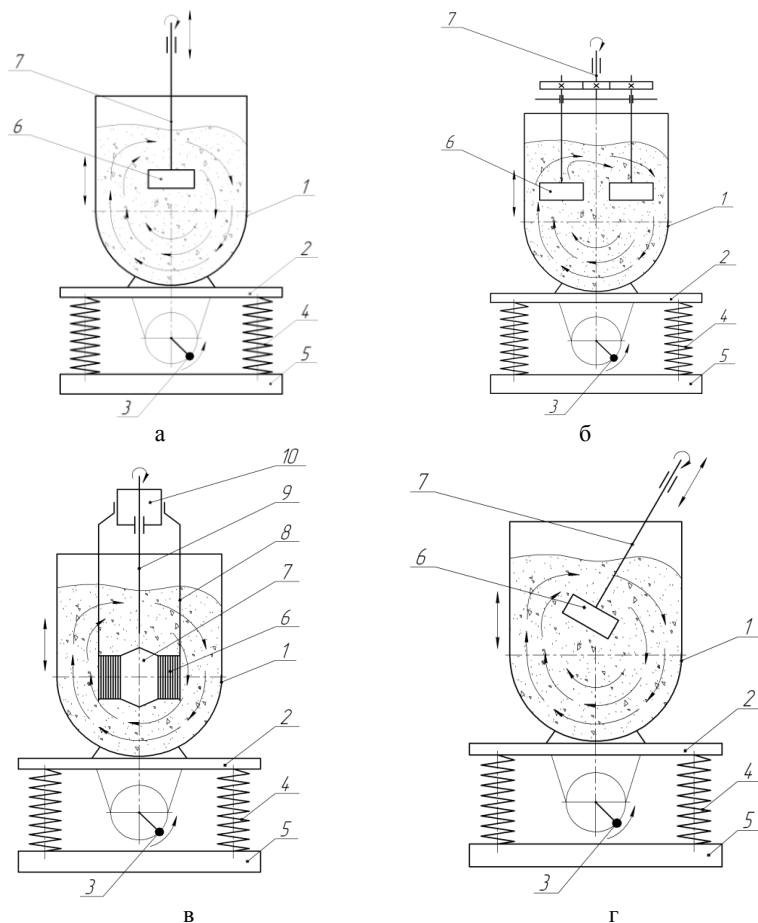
Схемы установки обрабатываемых деталей при шпиндельной виброобработке: 1 – резервуар; 2 – виброплатформа; 3 – вибровозбудитель; 4 – упругая подвеска; 5 – основание; 6 – обрабатываемая деталь; 7 – шпиндель; 8 – крепежное приспособление; 9 – инструмент; 10 – пиноль
